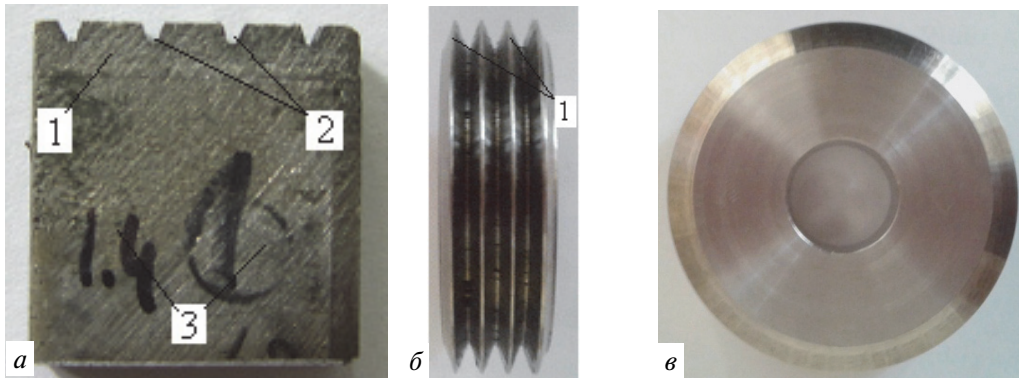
Образцы модельного трибосопряжения: *а* — пластина с покрытием: 1 — покрытие; 2 — результат изнашивания; 3 — тело пластины; *б* — диск, вид спереди: 1 — выступы профиля; *в* — диск, вид сверху
